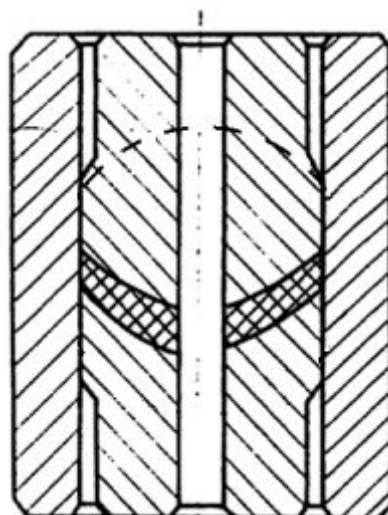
Процесс прессования УДЭ колоколообразной формы: - - - заготовка УДЭ; — — прессовка
